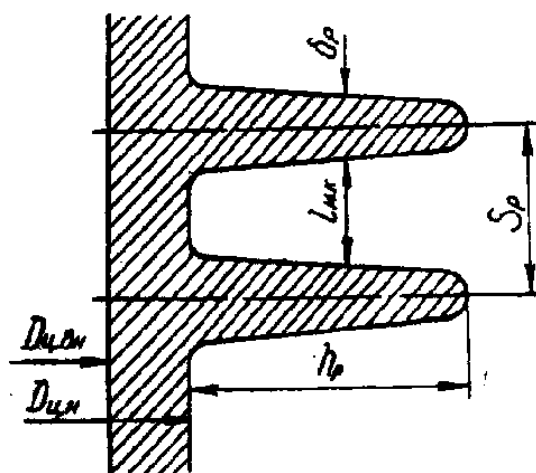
Расчетная схема оребрения цилиндров двигателя воздушного охлаждения
